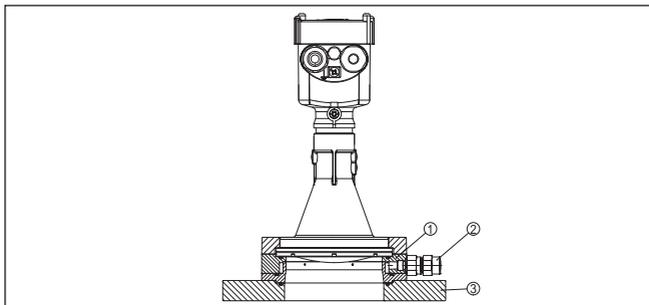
Conexão de limpeza no sensor de radar com flange adaptador em outros tamanhos
